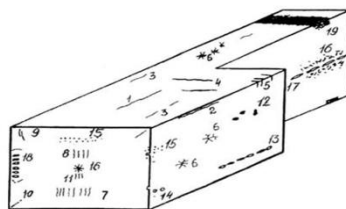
Схематическое представление основных видов дефектов непрерывнолитой заготовки
